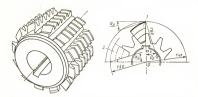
Конструктивные параметры задней поверхности червячных фрез, у которых кривая затылования является дугой окружности: I—зуб рейки в рабочем положении; 2—зуб рейки при обработке вадней поверхности.
